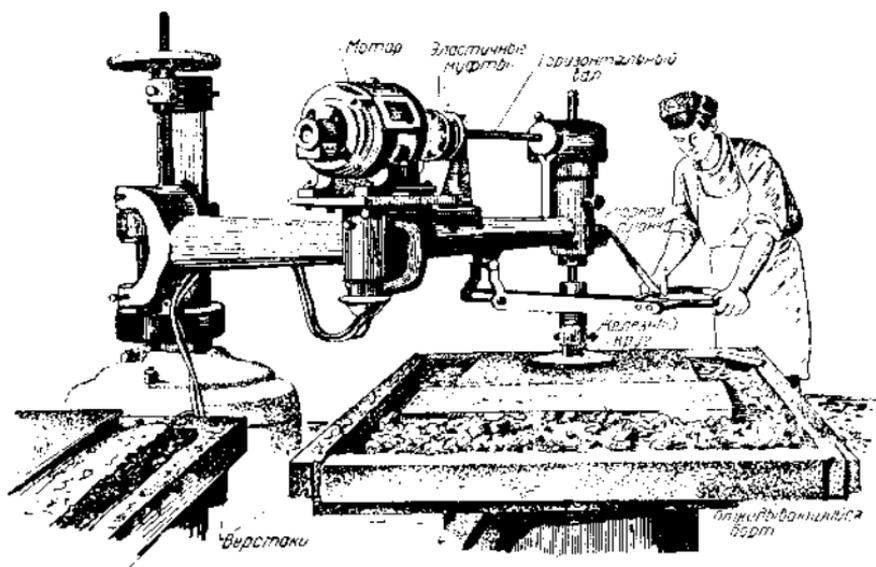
Вид колонкового шлифовально-полировочного станка с установленными двумя верстаками
